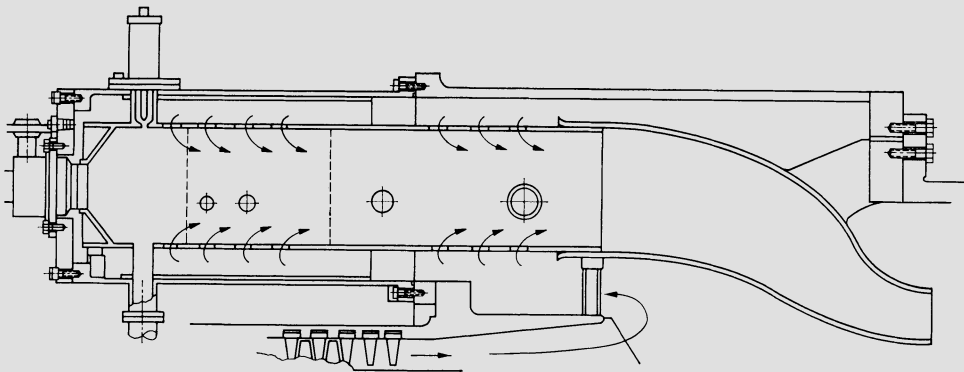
Brennkammer von General Electric. Bis zu 12 dieser Brennkammern sind ringförmig um die Maschinenachse angeordnet
